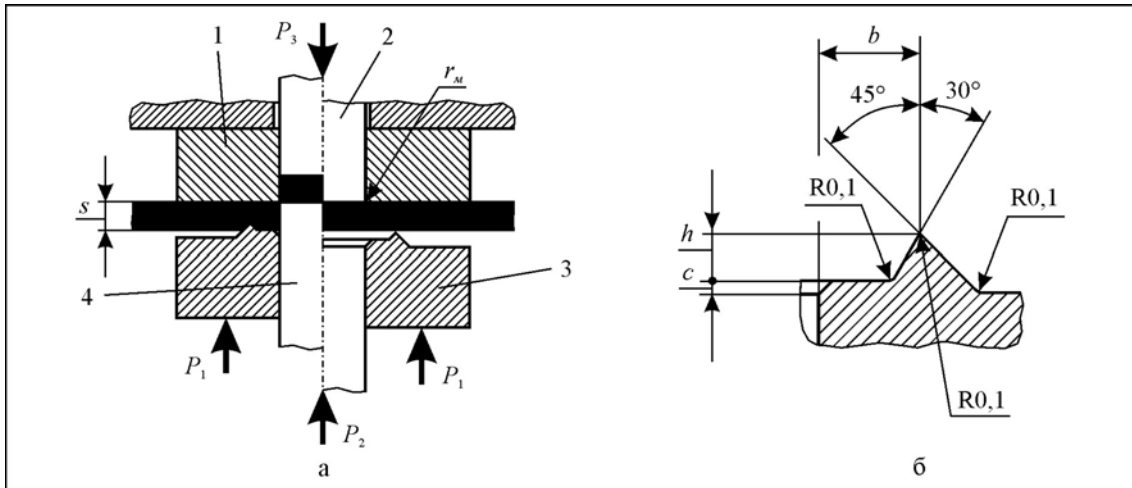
Схема штампа для чистового вирубання: а – схема; б – конструктивне виконання клинового ребра; 1 – матриця; 2 – контрпуансон; 3 – притискне кільце; 4 – пуансон
